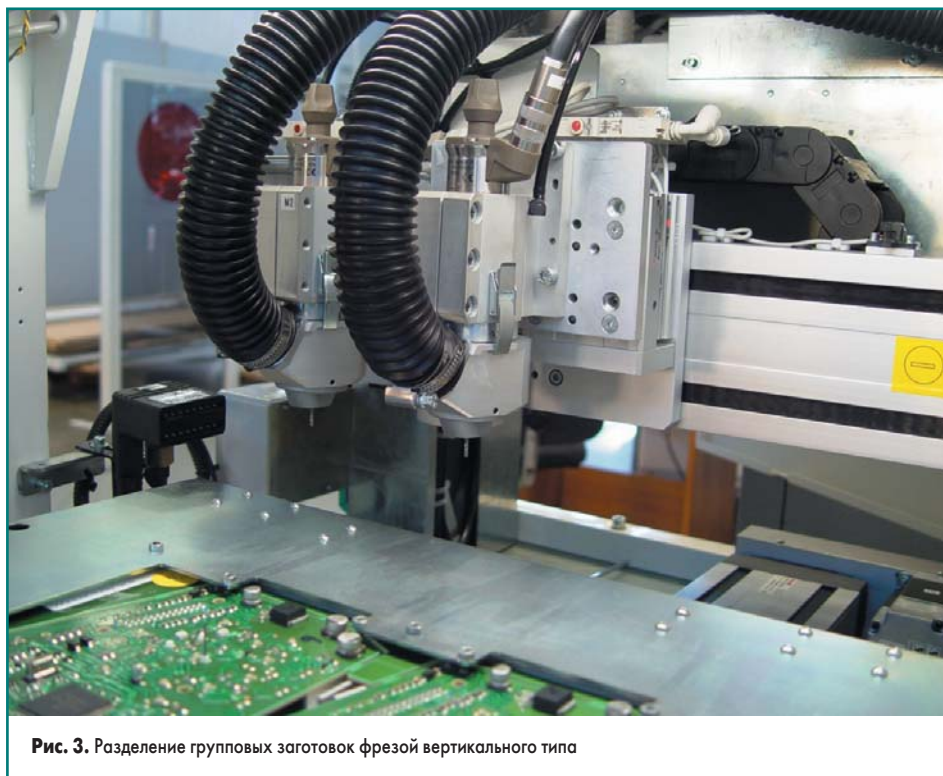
Разделение групповых заготовок фрезой вертикального типа
